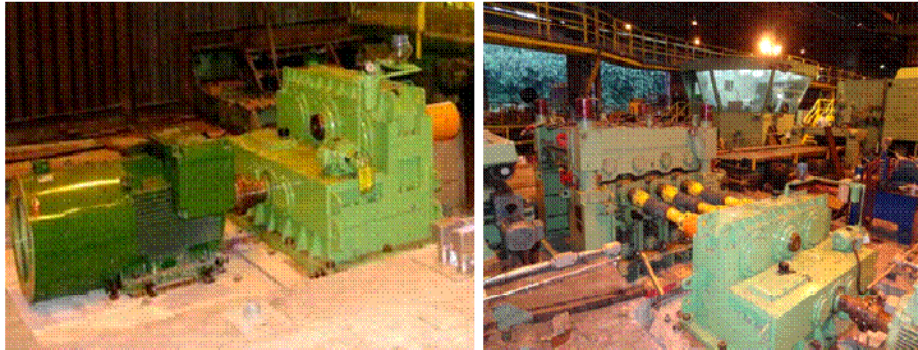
Motor – Redutor – Despenadeira Instalados.
